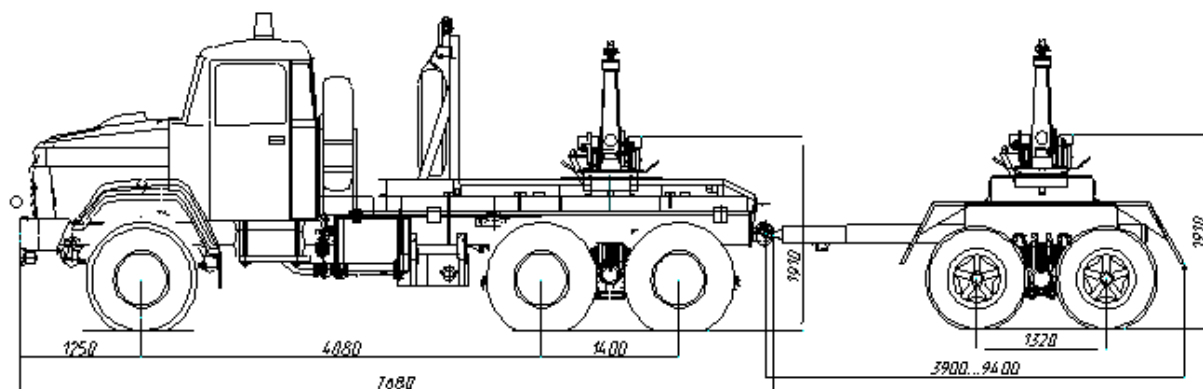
Саморазгружающийся автопоезд-металловоз на базе полуприцепа Т-38
